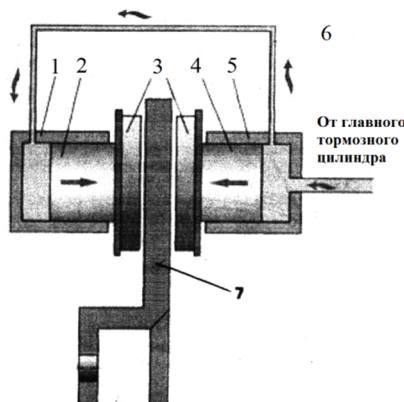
Схема дисково-колодочного тормоза: 1, 5 – колесные цилиндры; 2, 4 – поршни; 3 – тормозные колодки с накладками; 6 – трубопровод; 7, 8 – тормозной диск с фланцем
